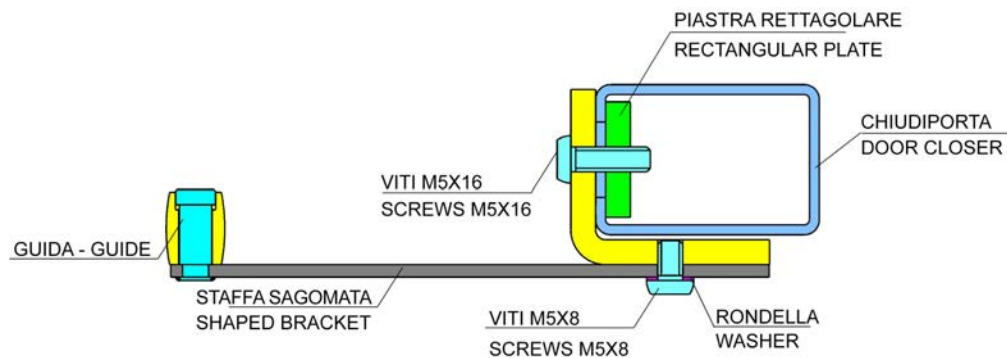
Schema di montaggio della staffa con oliva sul chiudiporta - Scheme between the bracket with roller and the door-closer
